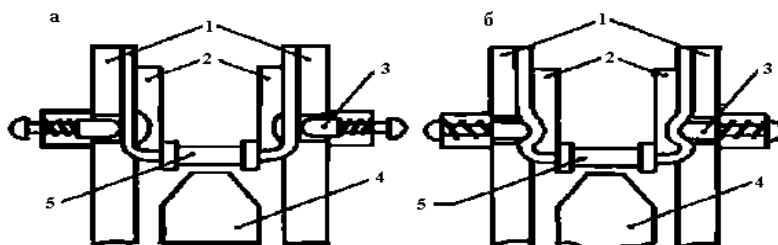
Схема для "зиг" – формовки выводов радиоэлементов:
